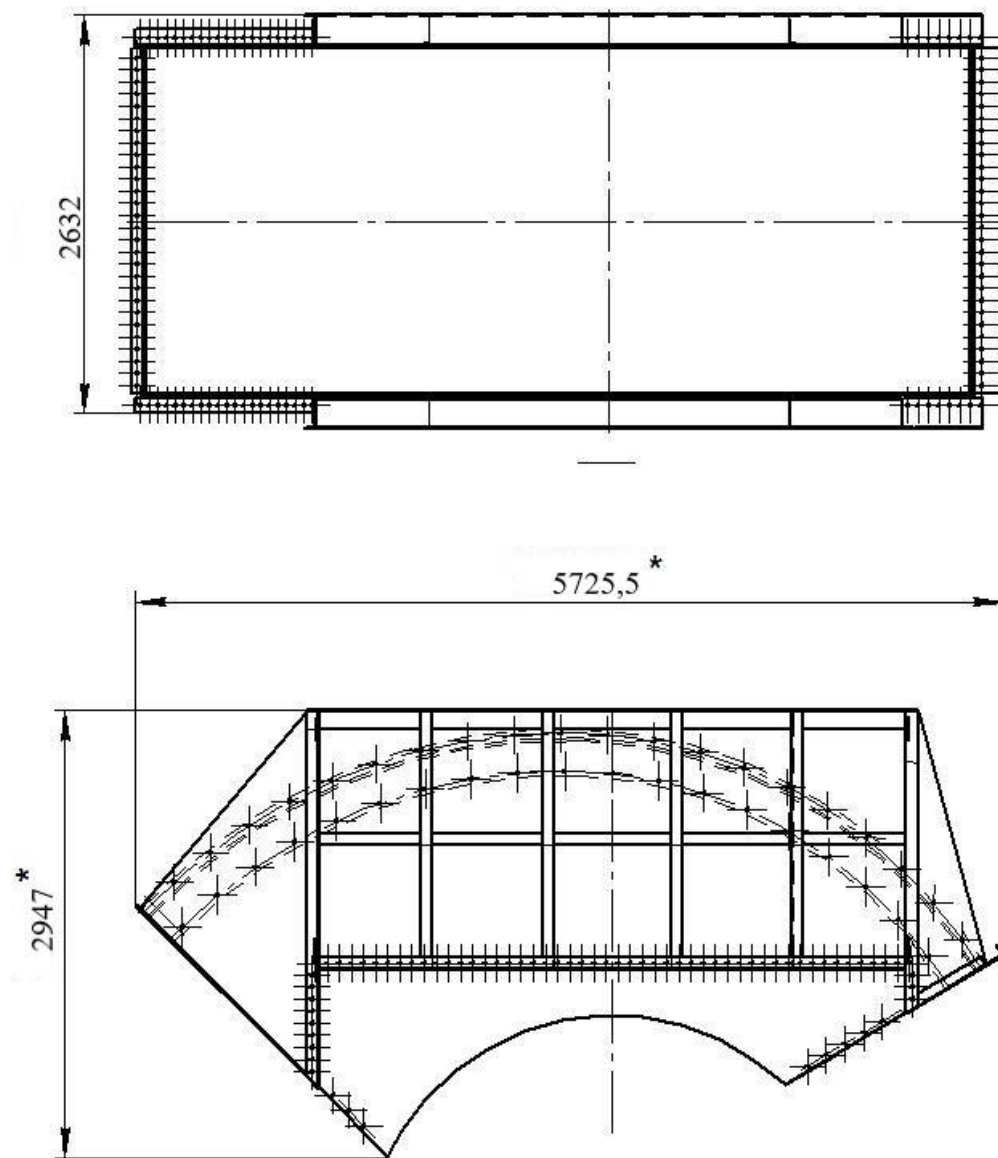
Рама корпусу (див. креслення НУЗП 443423.001 СК)
